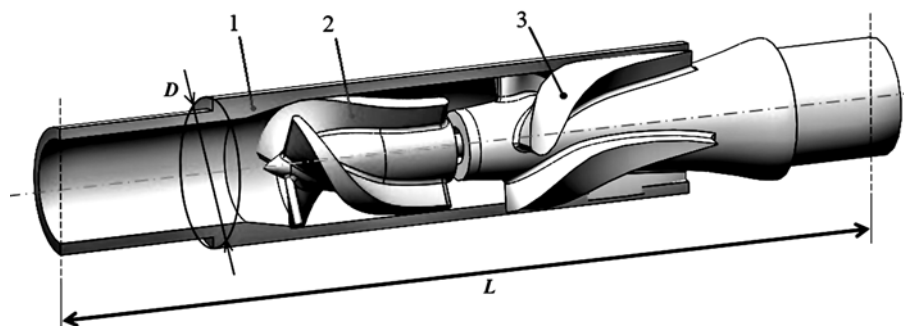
Внешний вид прототипа микронасоса: 1 – корпус; 2 – рабочее колесо; 3 – спрямляющий аппарат
